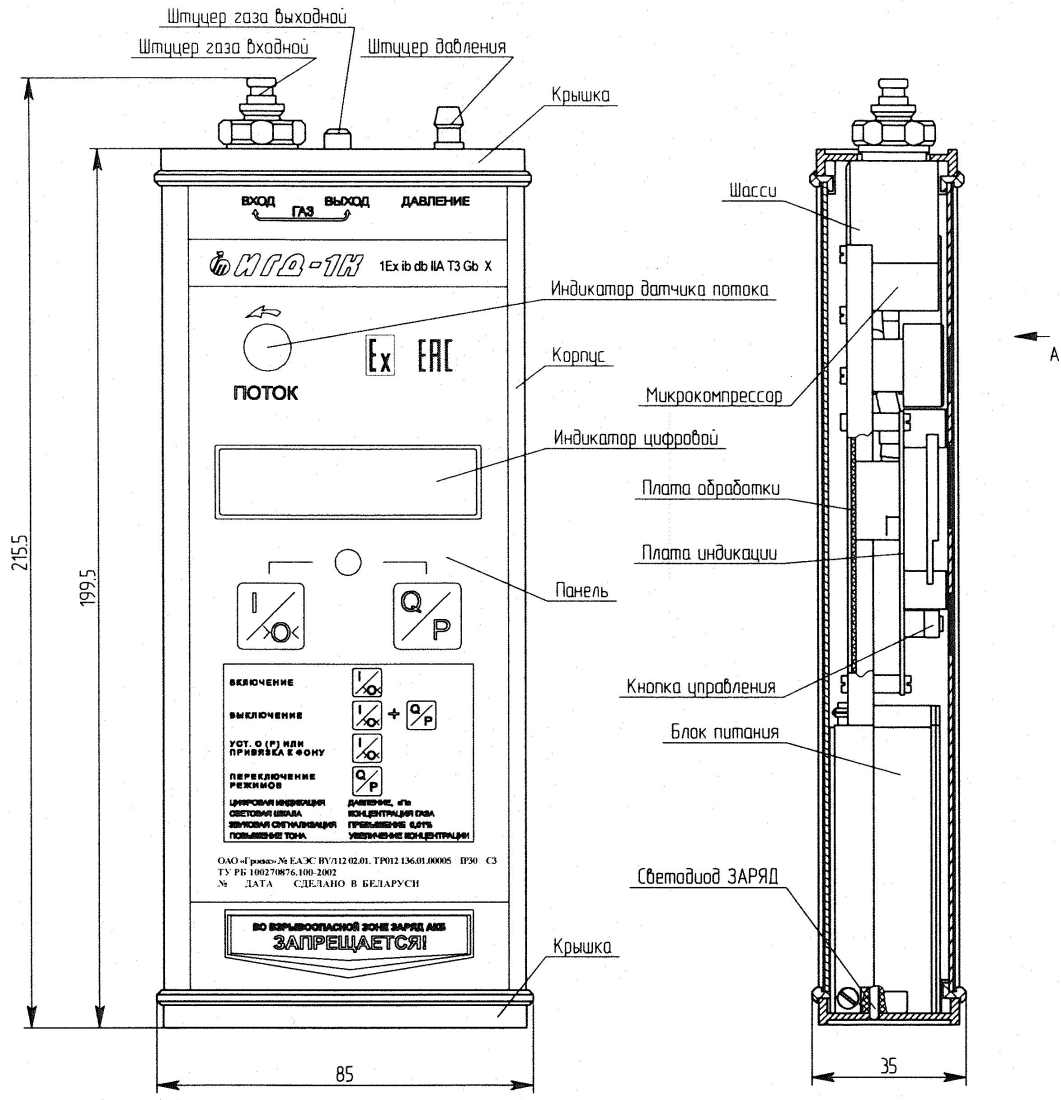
Внешний вид индикатора ИГД-1К
